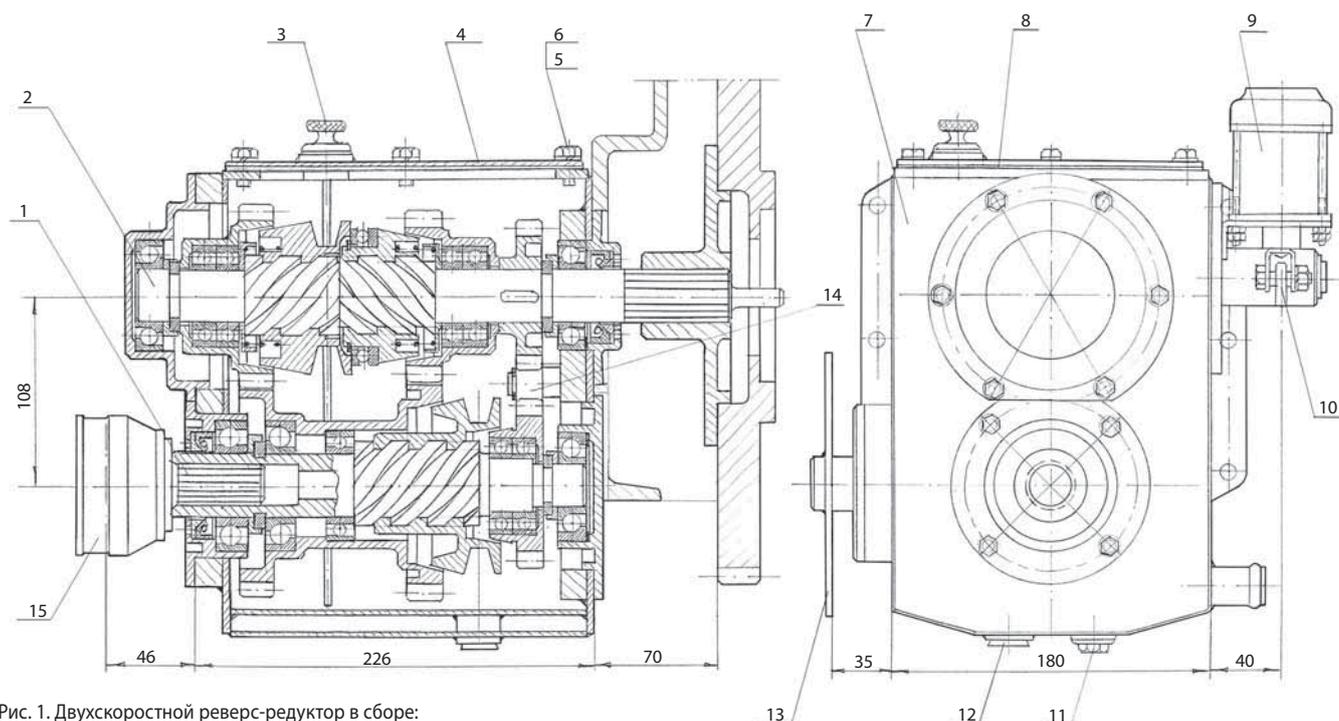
Двухскоростной реверс-редуктор в сборе:
